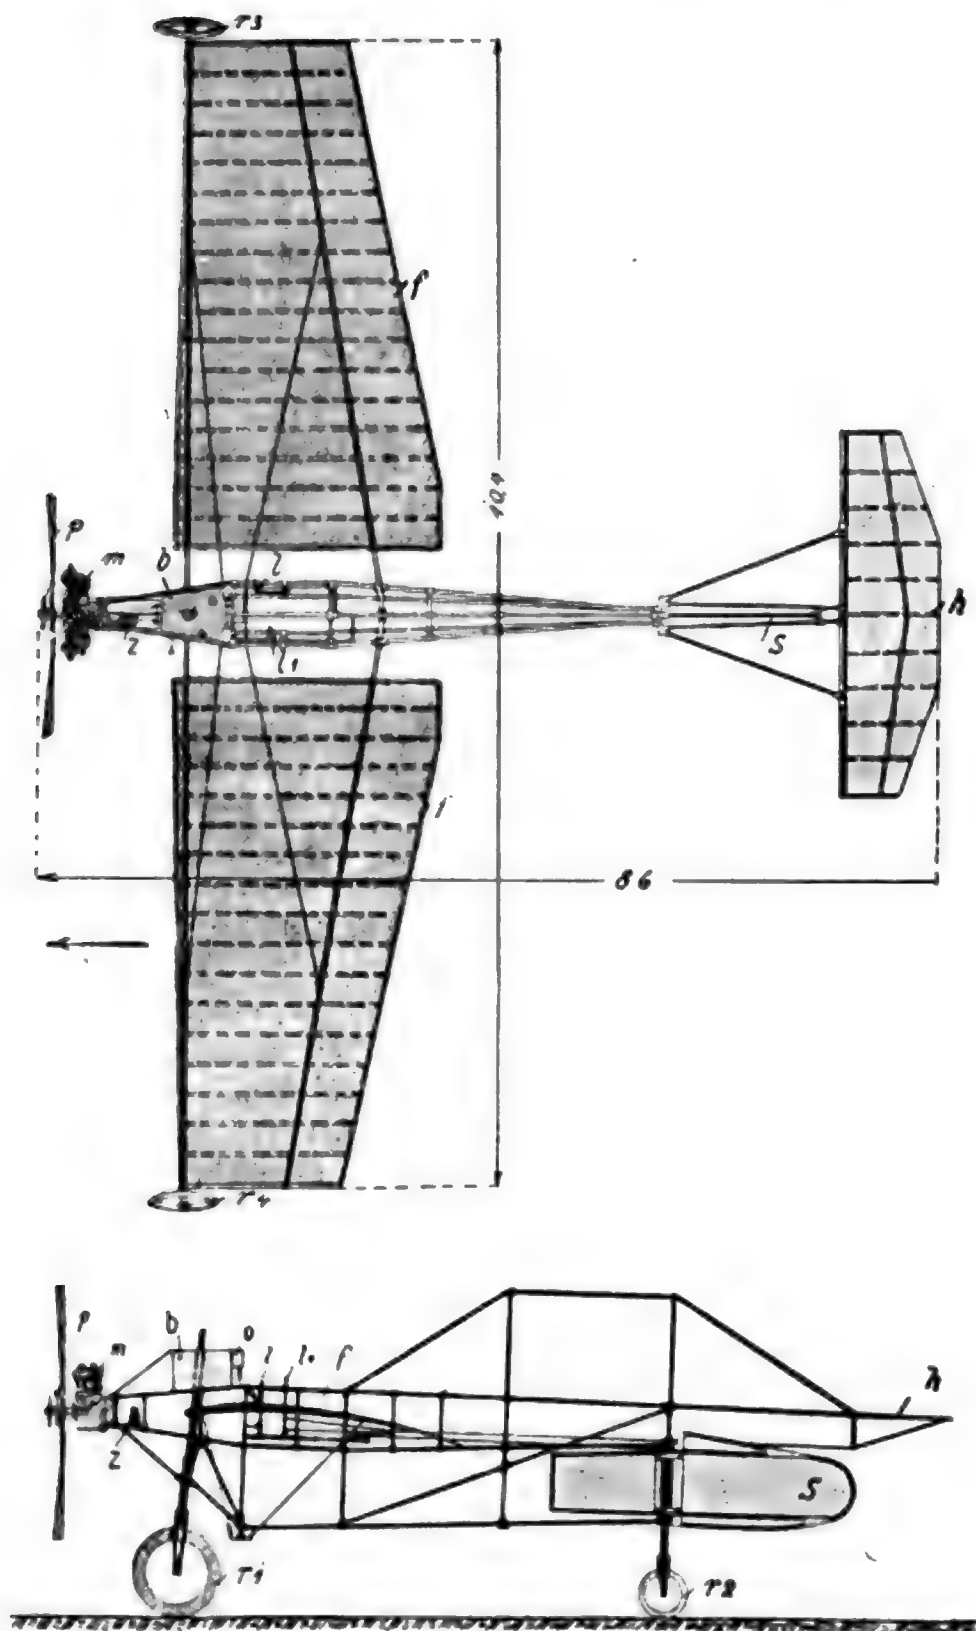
und 189. Zeichnung des Eindeckers System Esnault-Pelterie. Ansicht von oben und Seitenansicht.
